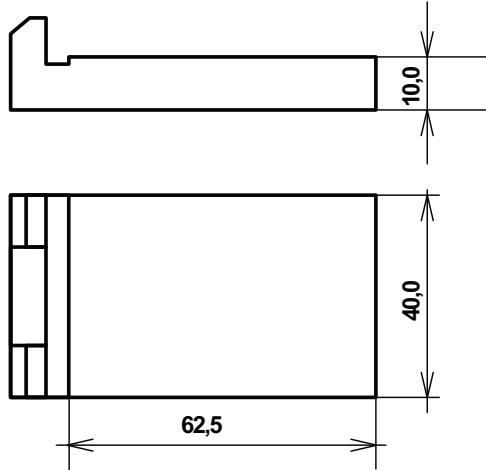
Пластины для передачи нагрузки на половинки образцов-балочек
